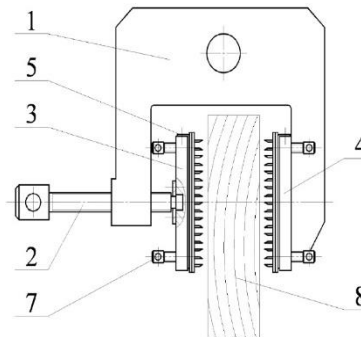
Грузозахватное устройство с ошипованными контактными элементами для перемещения деревянных конструкций: 1 — П-образный корпус; 2 — зажимной винт; 3 — подвижный контактный элемент; 4 — неподвижный контактный элемент; 5 — металлическая зубчатая пластина; 7 — отжимной винт; 8 — перемещаемая деревянная конструкция
